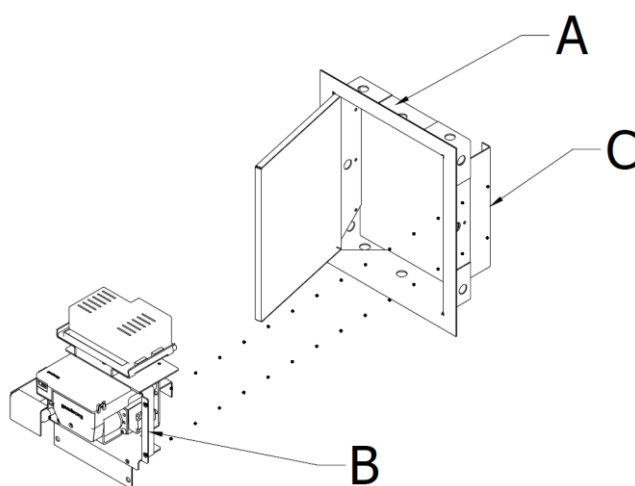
Instalación del conjunto de gas en la trampilla de inspección
